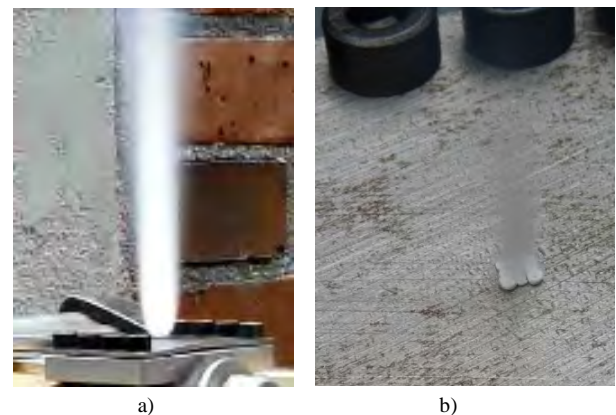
Ausströmendes, flüssig zugeführtes CO_2 durch a) eine mechanisch erzeugte Bohrung mit Durchmesser 1 mm und b) 9 lasergefertigte Mikrobohrungen mit Austrittsdurchmesser von 55 μm .
